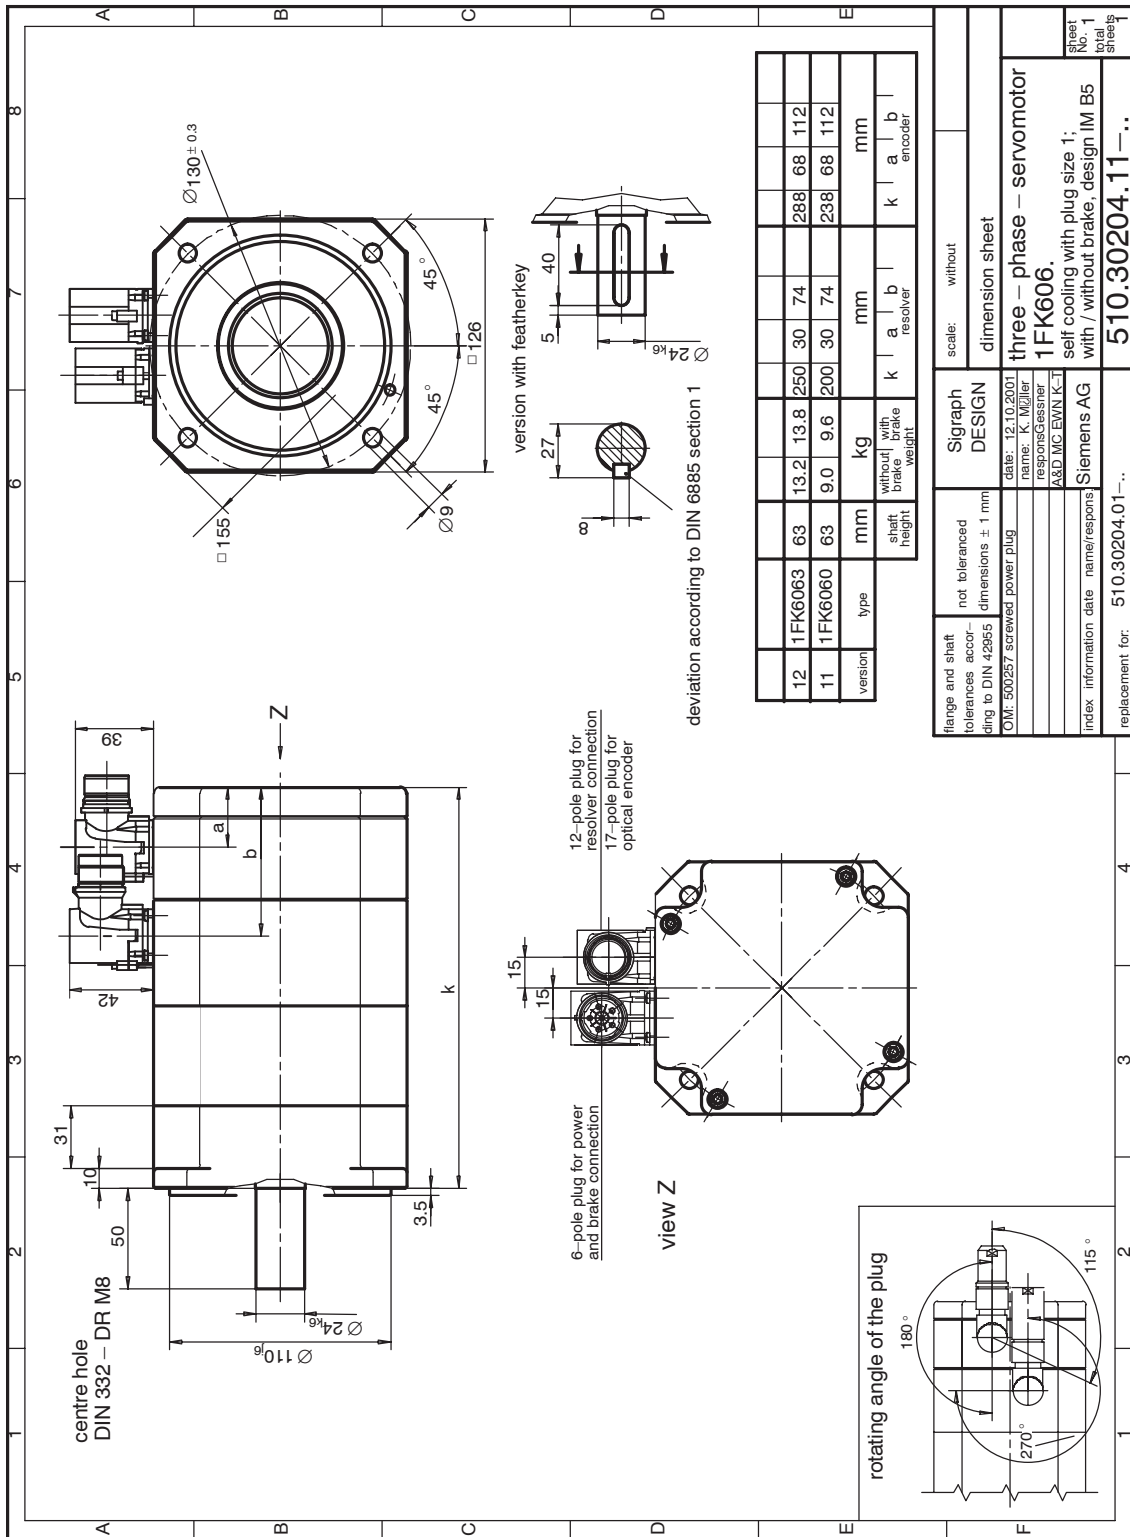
1FK606 □ Standard, selbstgekühlt mit abgewinkeltem Stecker Größe 1
